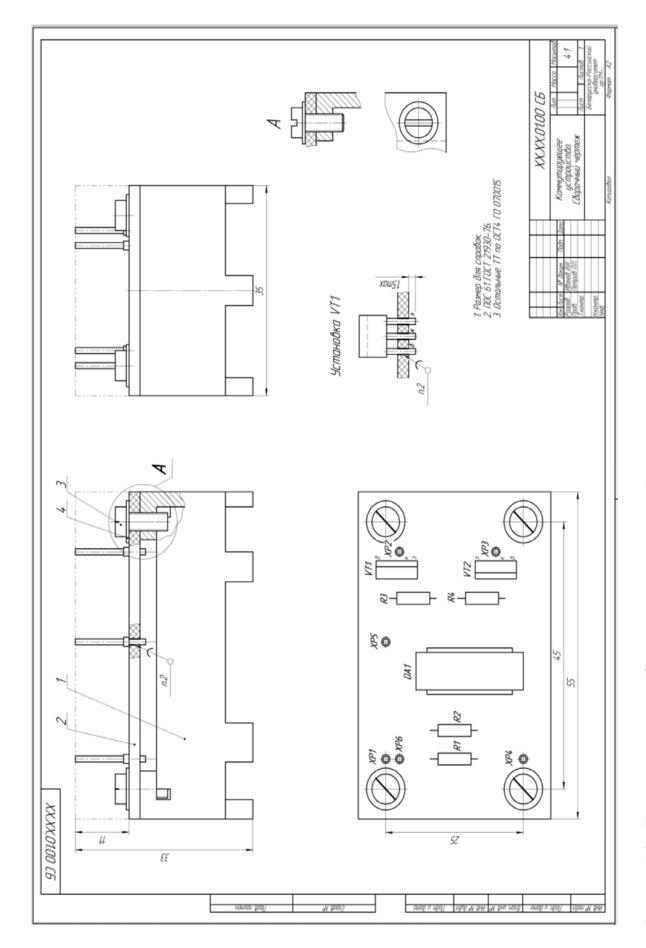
Пример выполнения сборочного чертежа печатной платы
